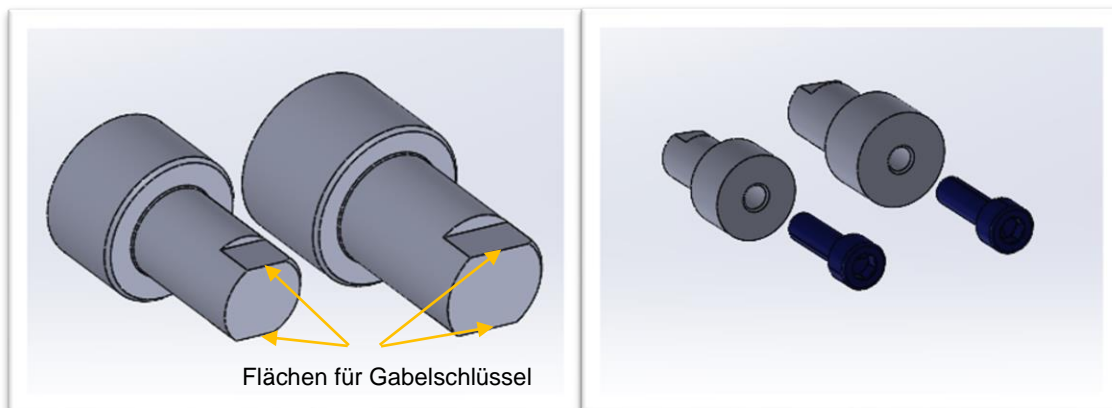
Anschlagbolzen mit Zylinderschraube M6x20 mm Befestigung
